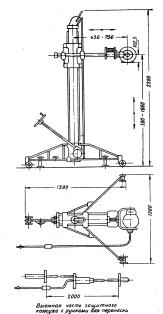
Габаритные размеры гамма аппарата ГУП-Со-0,5-1
